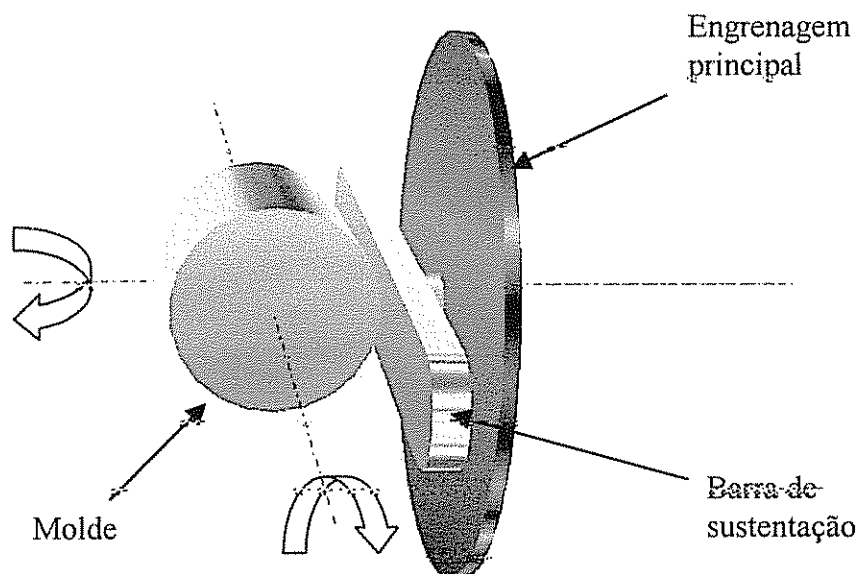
9: movimento bi-axial a que o molde está sujeito durante a cura
